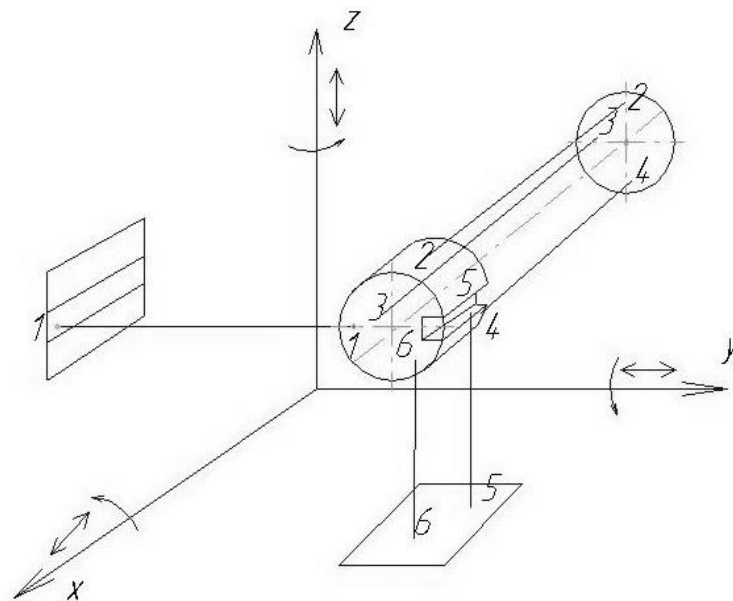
Схема базування циліндричної заготовки зі співвідношенням $l/d < 1$
